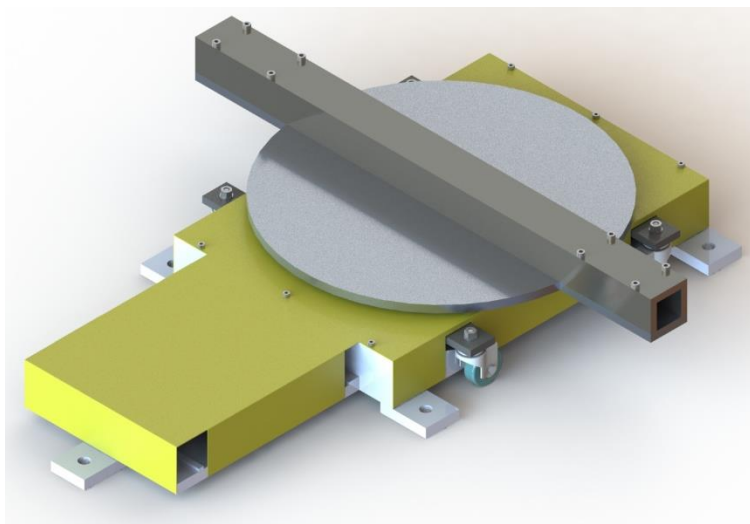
Esboço final do sistema rotativo da estrutura metálica para paletização dos painéis de porta.
